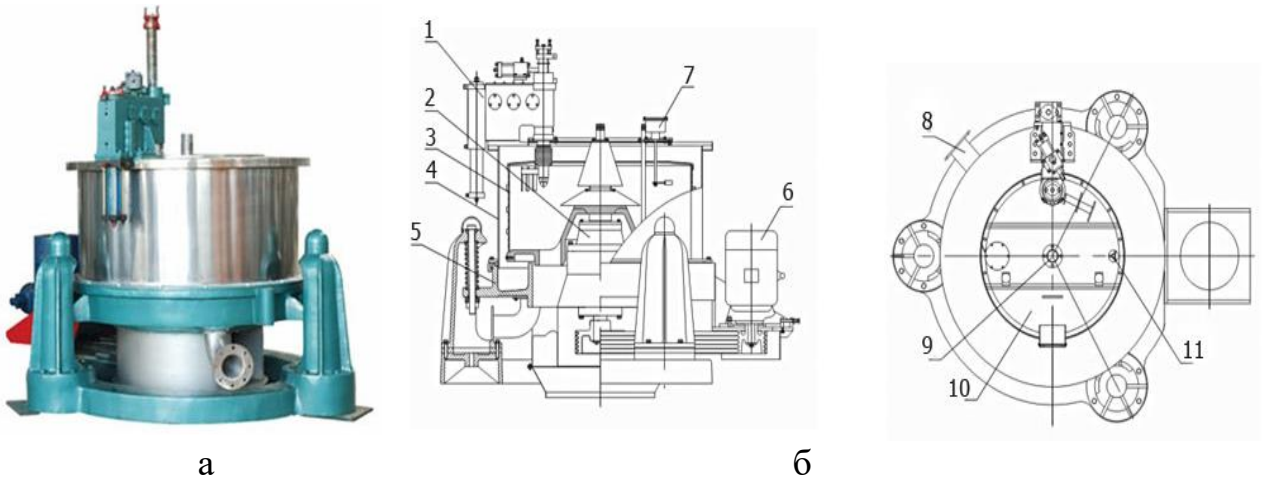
Триколонна центрифуга зі скребками і нижнім вивантаженням (а) та її принципова схема (б): 1 - ніж (скребок); 2 - вал; 3 - барабан; 4 - корпус; 5 - станина; 6 - мотор; 7 - контроль рівня кеку; 8 - зливний отвір; 9 - труба подачі матеріалу; 10 - мала кришка; 11 - промивальна труба
